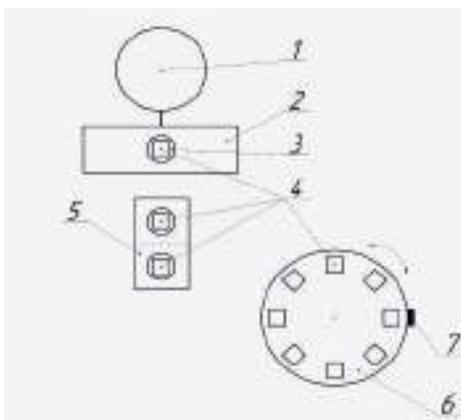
Гибкий производственный модуль на базе многооперационного станка с ЧПУ ИР800МФ4: 1 – шпиндельный узел станка; 2 – рабочий стол; 3 – поворотный стол; 4 – паллеты; 5 – вспомогательный двухпозиционный стол-спутник; 6 – стол-накопитель – тактовый стол; 7 – порт стола-накопителя
